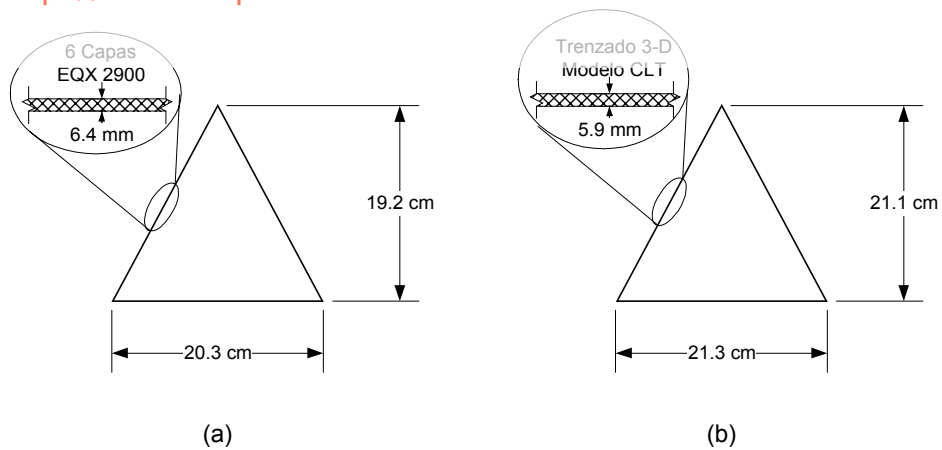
Detalles de las secciones de los modelos de elementos finitos para vigas triangulares: a) NCF, b) trenzado 3-D.
